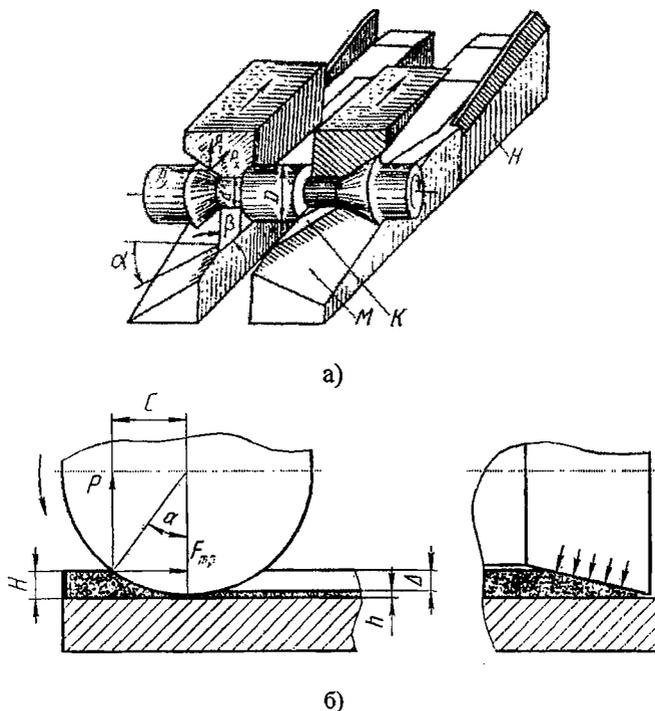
Схемы поперечно-клиновой прокатки (а) и действия сил, возникающих на площадке контакта конического вала с заготовкой (б)
